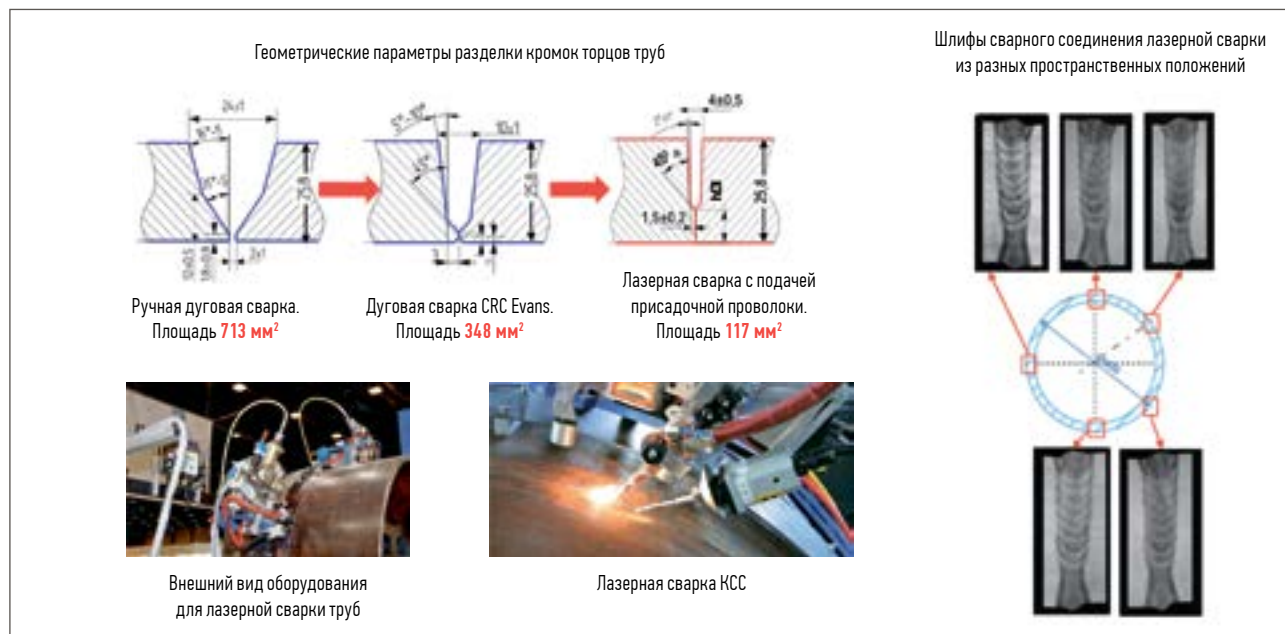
Инновационная отечественная технология лазерной сварки неповоротных кольцевых стыковых соединений труб
